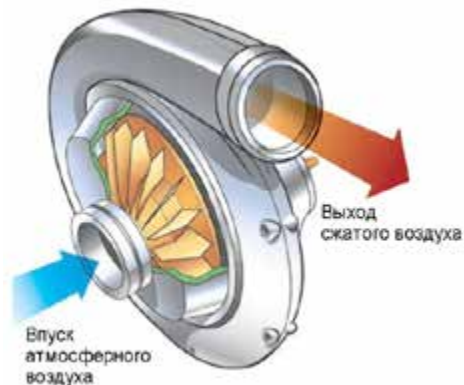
Центробежный нагнетатель, представляет собой корпус с расширяющимся объемом – «улиткой», внутри которой вращается центробежная крыльчатка. Воздух попадает в центральное отверстие корпуса и затем отбрасывается в стороны от центра быстро вращающейся крыльчаткой компрессора.
